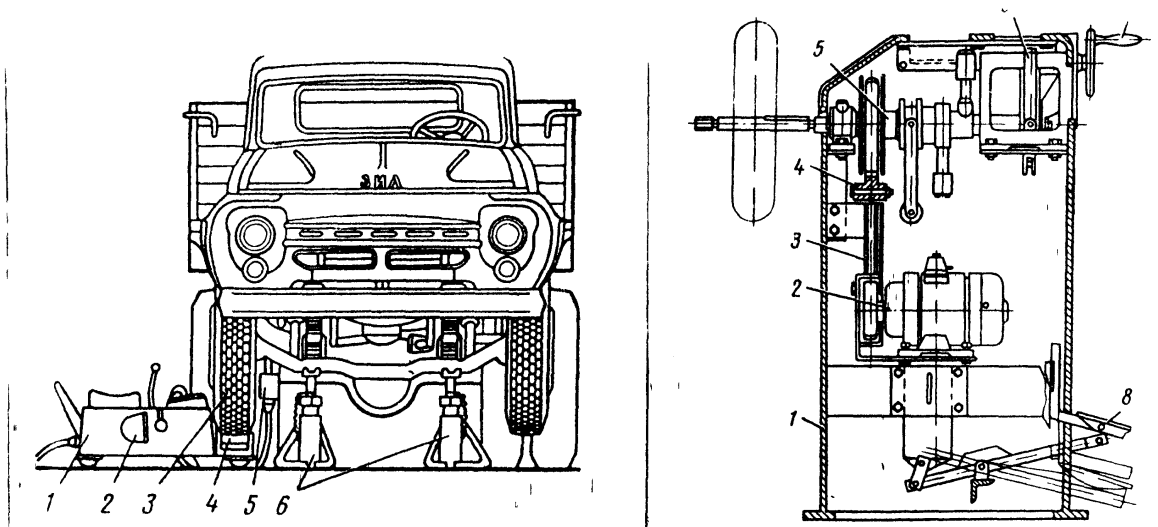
Схема динамической балансировки колес и устройство балансировочного станка
